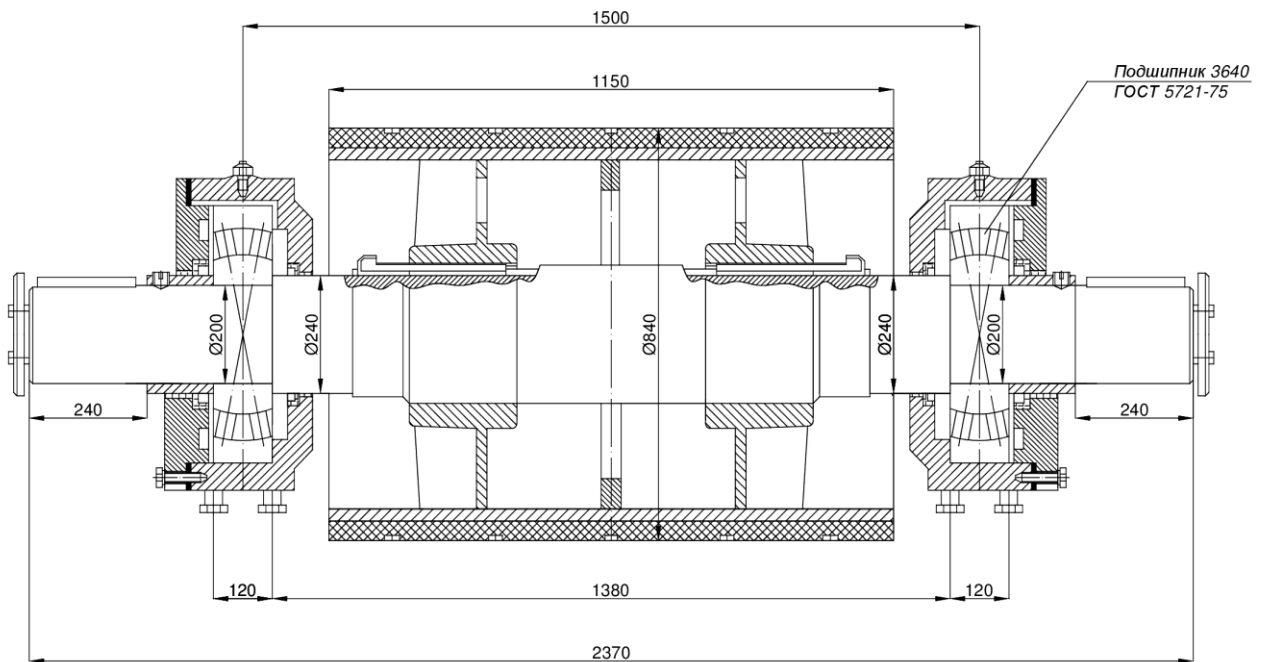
Барабан ленточного конвейера с дополнительным диском: 1 – обечайка; 2 – усиливающий диск; 3 – стопорный винт; 4 – ступица; 5 – торцевое кольцо; 6 – крепежный винт; 7 – шейка вала; 8 – вал
